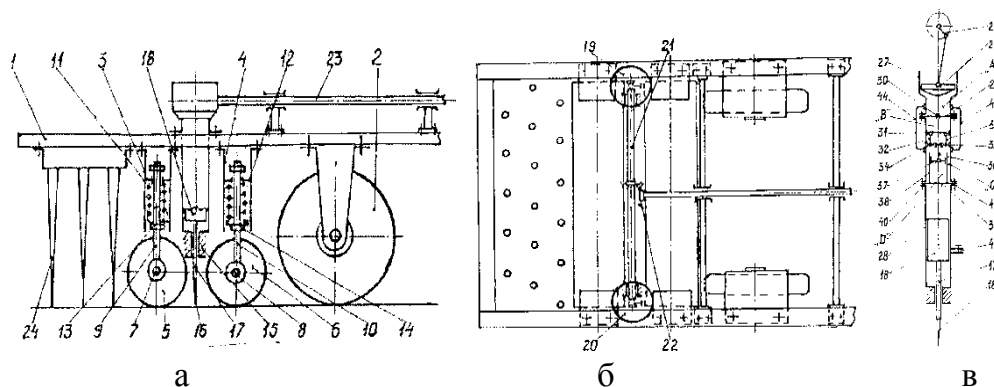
Конструкція пневмомеханічного подрібнювача рослинних стебел на поверхні поля: а - вигляд збоку; б - вигляд зверху; в - загальний вигляд в розрізі пневмомеханічного привода
